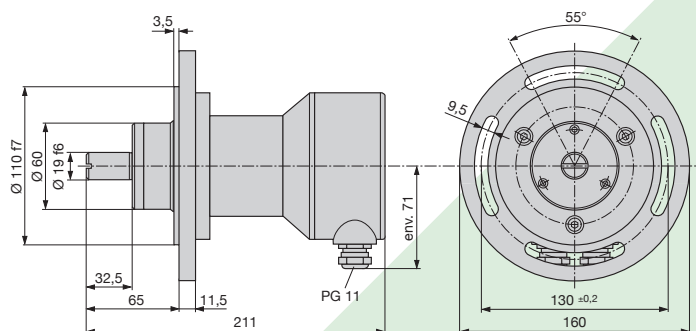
KINAX WT 707 avec engrenage additionnel, bornes à vis, ainsi que presse-étoupes et flasque.
